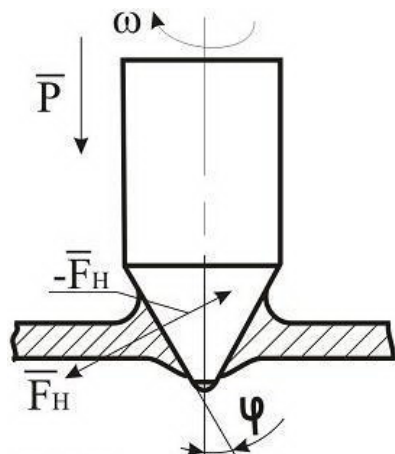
Схема взаимодействия инструмента с заготовкой при пластическом сверлении
